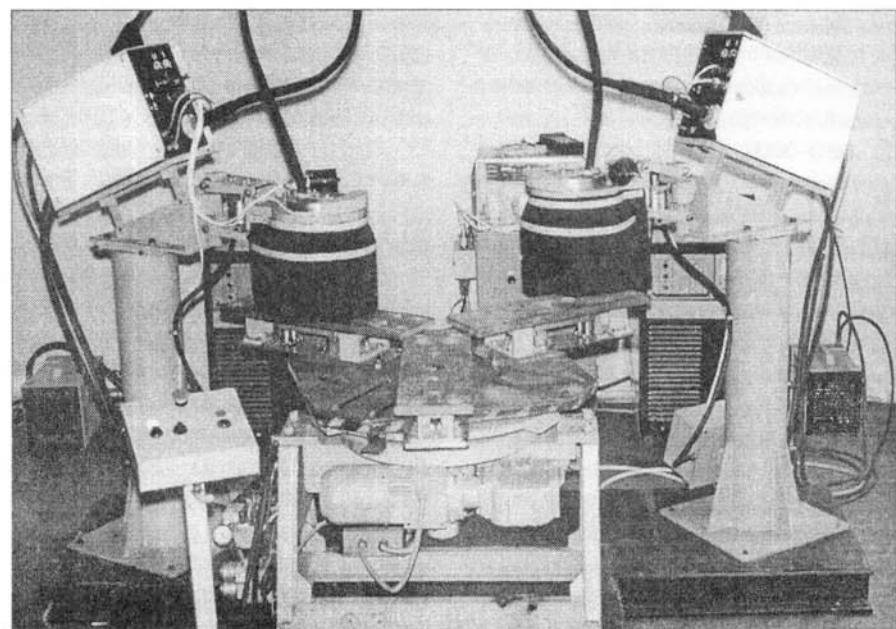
Установка для автоматической дуговой сварки подушки с подкладкой
